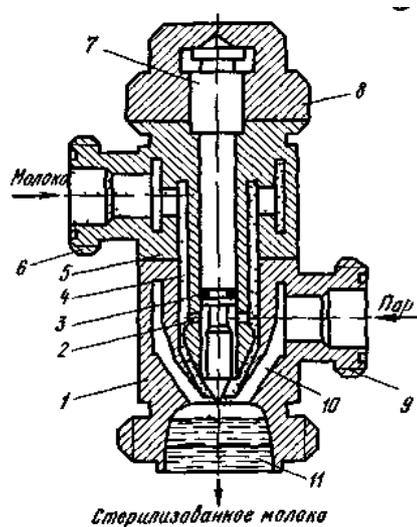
Схема нагревателя инъекционного типа (пар в молоко): 1 — корпус нагревателя; 2 — отверстие для молока; 3 — уплотнительное кольцо; 4 — кольцевой канал для молока; 5 — корпус нагревателя; 6 — патрубок для ввода молока; 7 — центральный стержень; 8 — регулировочная гайка; 9 — патрубок для ввода пара; 10 — канал для пара; 11 — камера смешения
